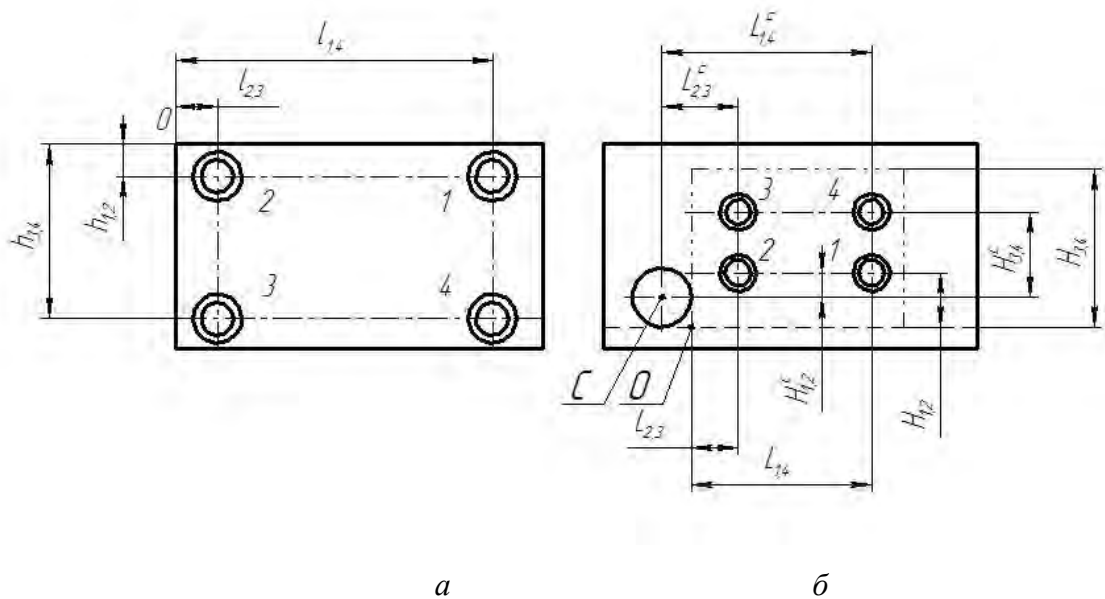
Схемы измерения детали (а) и приспособления (б)
